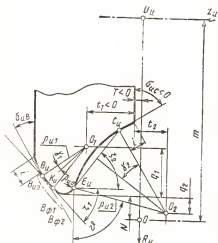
Схема замены дугами окружностей теоретического профиля дисковой фрезы для обработки винтовых канавок у цилиндрических фрез
